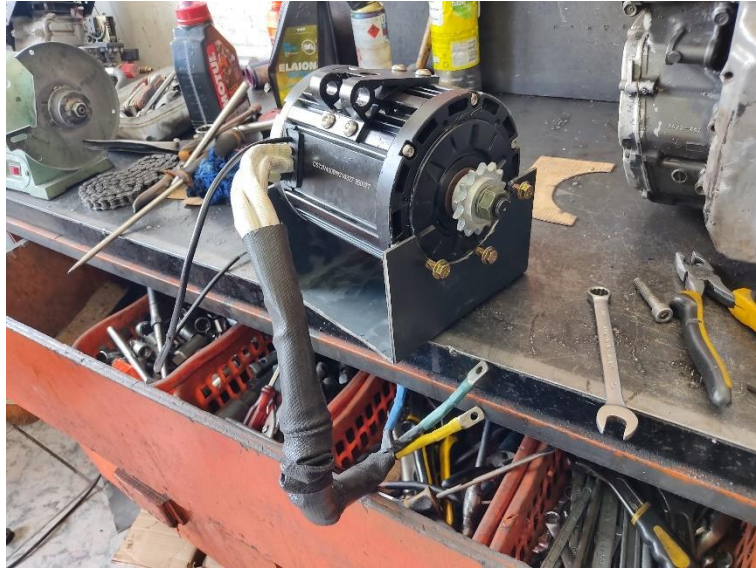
Montaje del motor eléctrico en la base diseñada
